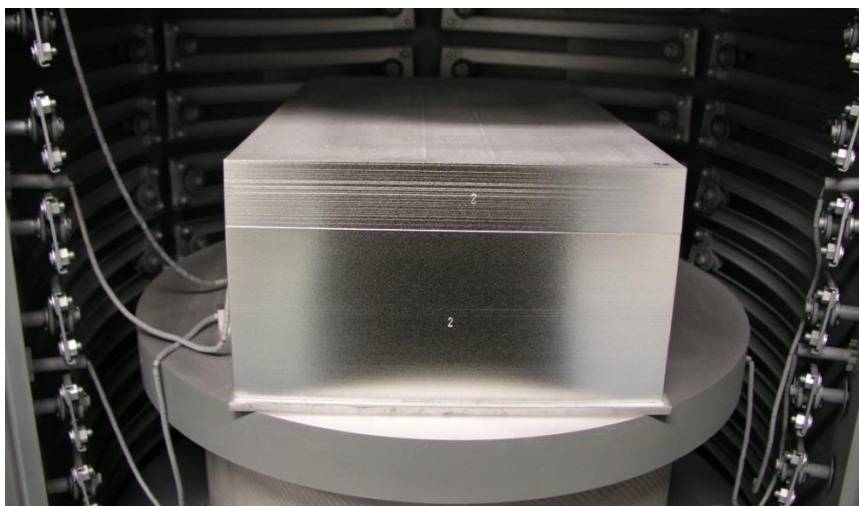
Versuchsteil im Schweißofen vor der Diffusionsschweißung.
